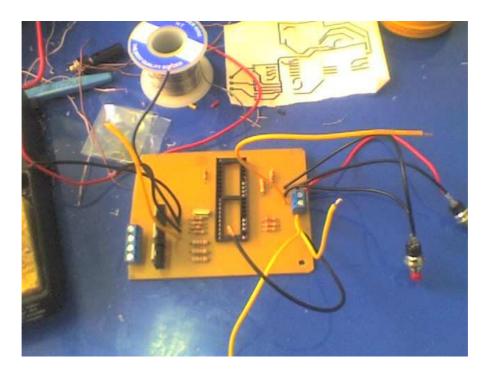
Elementos soldados Fuente: Desarrollo del proyecto
